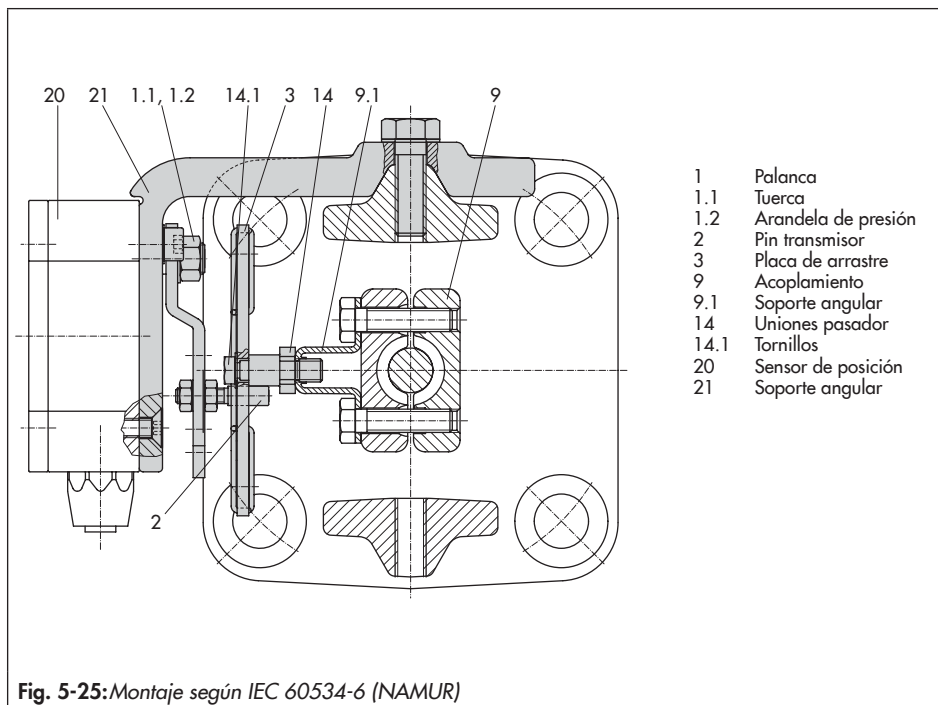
Montaje según IEC 60534-6 (NAMUR)
